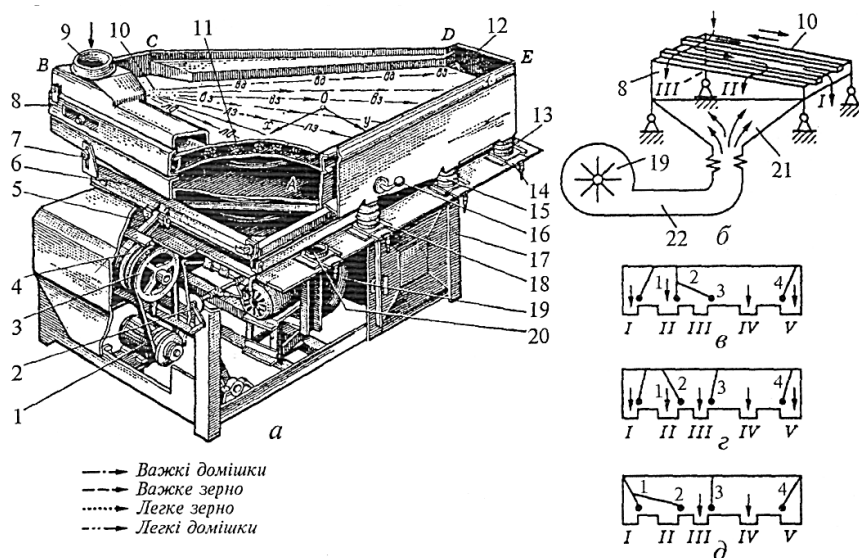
Пневматичний сортувальний стіл ПСС-2.5В:
